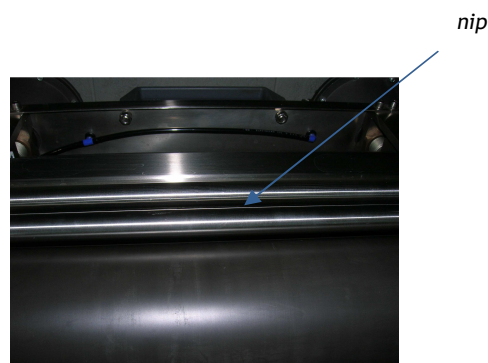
Pormenor dos rolos aplicadores da size press.
